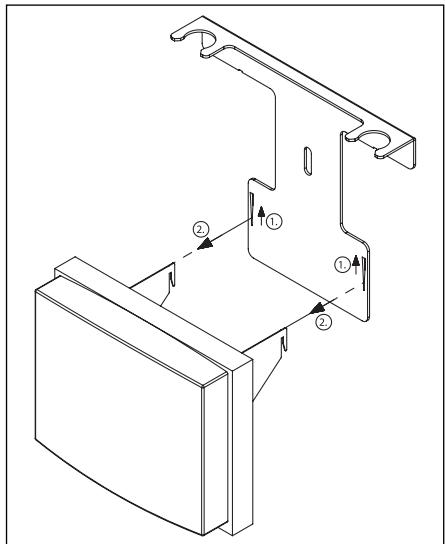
Démontage du couvercle aveugle avec tôle de retenue
